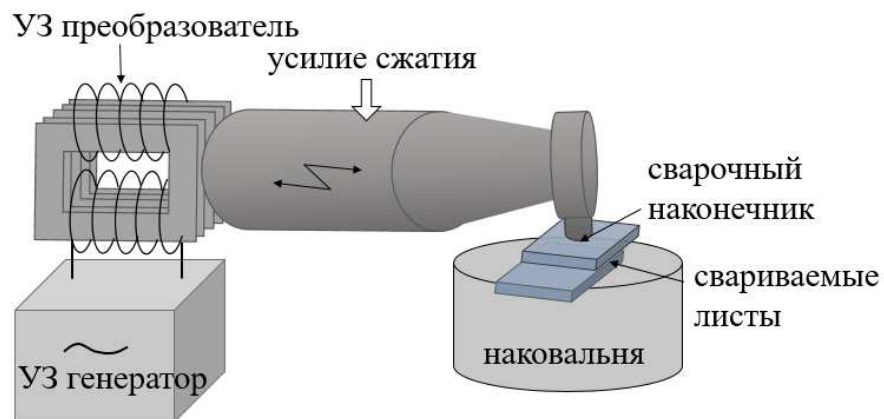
Принципиальная схема ультразвуковой сварки
